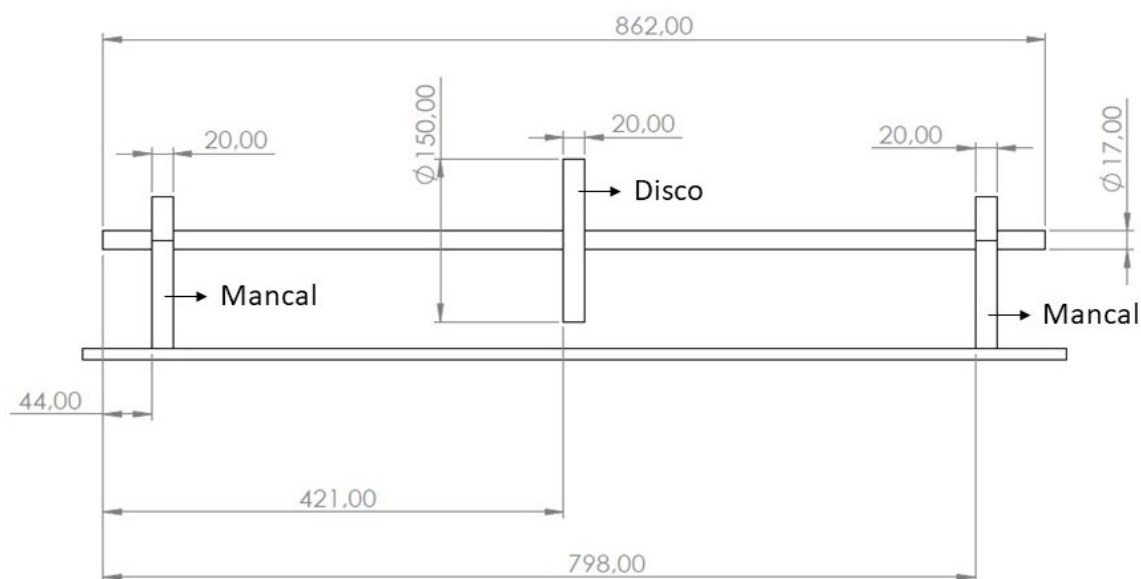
Vista lateral do rotor embarcado a ser simulado com dimensões em milímetros.
